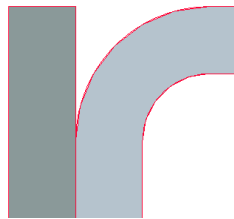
Sección transversal de la pieza. Acercamiento a la junta de soldadura.
